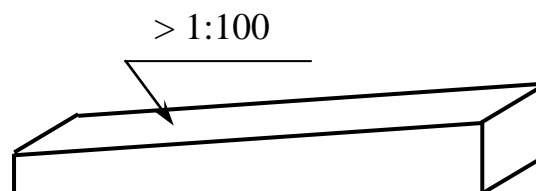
Зовнішній вигляд клинової шпонки
